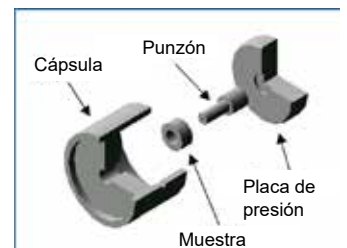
Fuente: Universidad Técnica de Darmstadt
